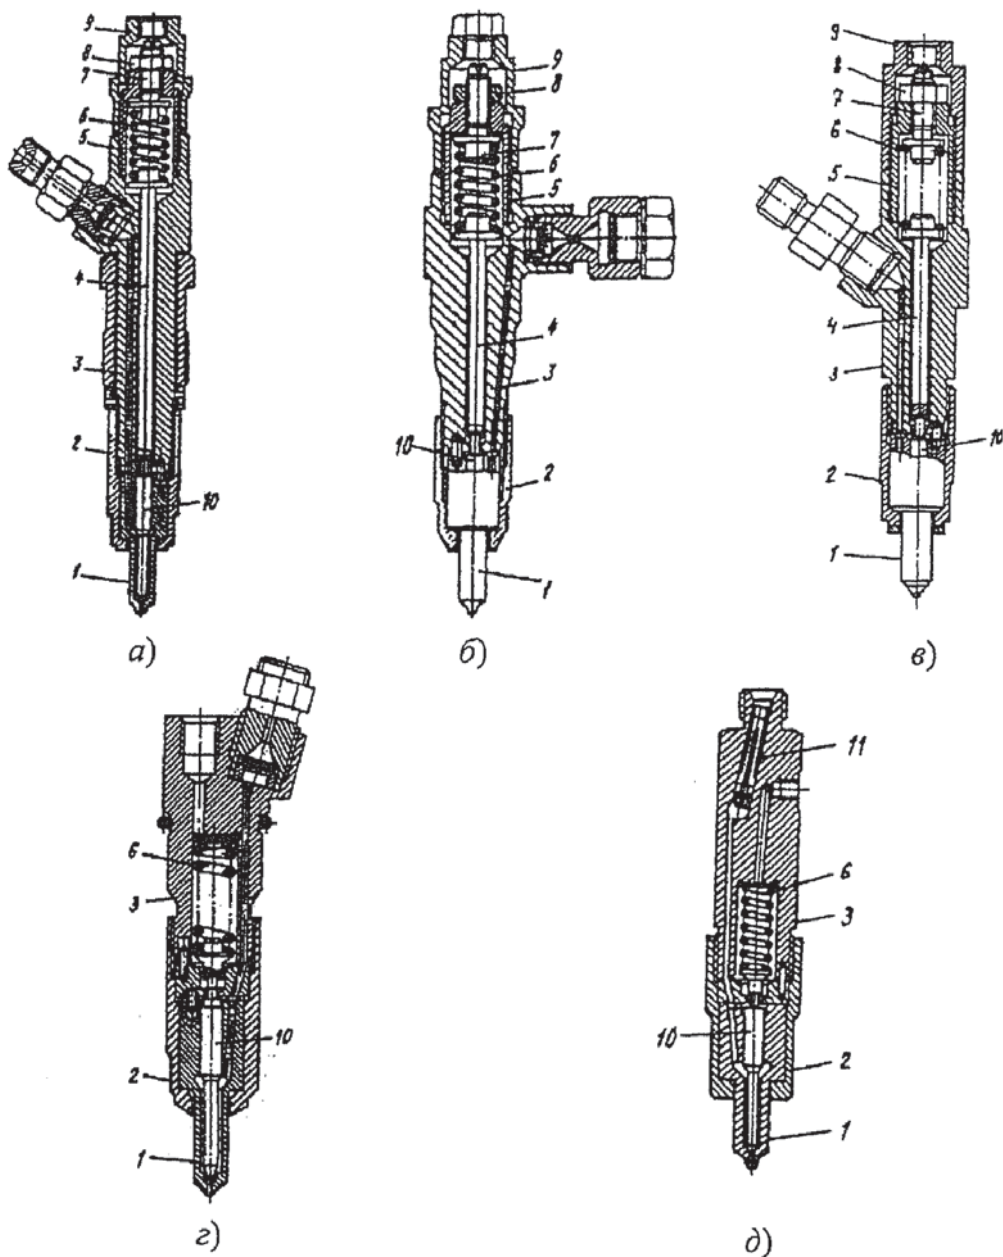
Многоструйные форсунки отечественных и зарубежных дизелей: а — 6Т2; б — 6А1; в — ФД-22; г — дизеля КамАЗ-740; д — фирмы R. Bosch: 1 — распылитель; 2 — накидная гайка; 3 — корпус форсунки; 4 — штанга; 5 — гайка пружины; 6 — пружина; 7 — регулировочный винт; 8 — контргайка; 9 — колпак; 10 — игла распылителя; 11 — щелевой фильтр
